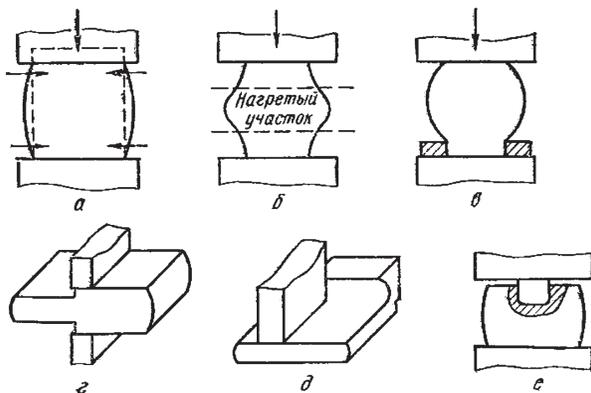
Операции свободнойковки: а – осадка; б, в – высадка; г – протяжка; д – разгонка; е – прошивка
